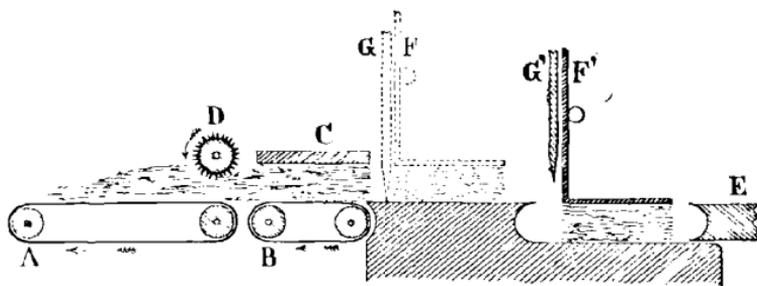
Machine Découste à bourrer les tubes sans colle.
